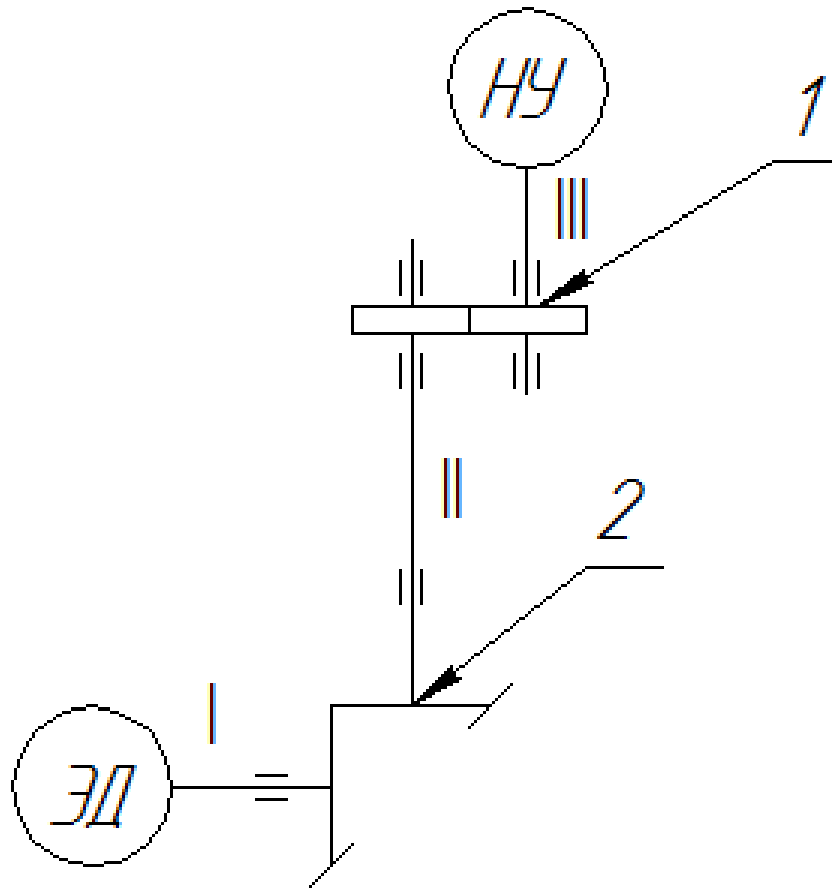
Кинематическая схема привода двигателя намоточного устройства
